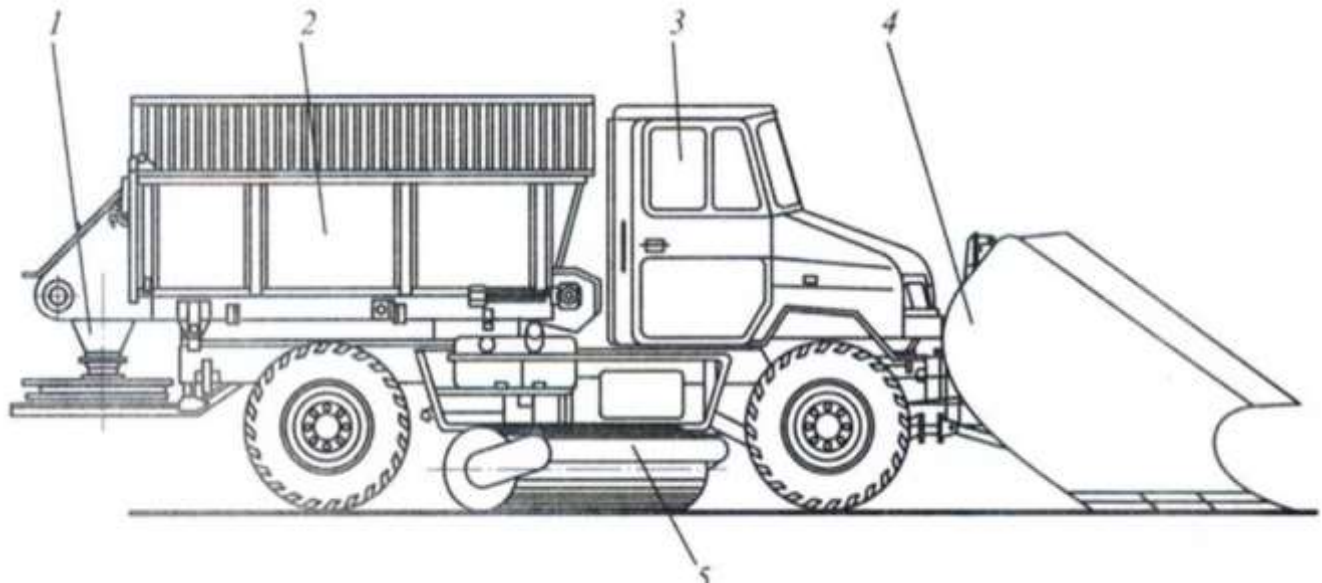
Снегоочиститель плужный, с подметальным оборудованием и пескоразбрасывателем
